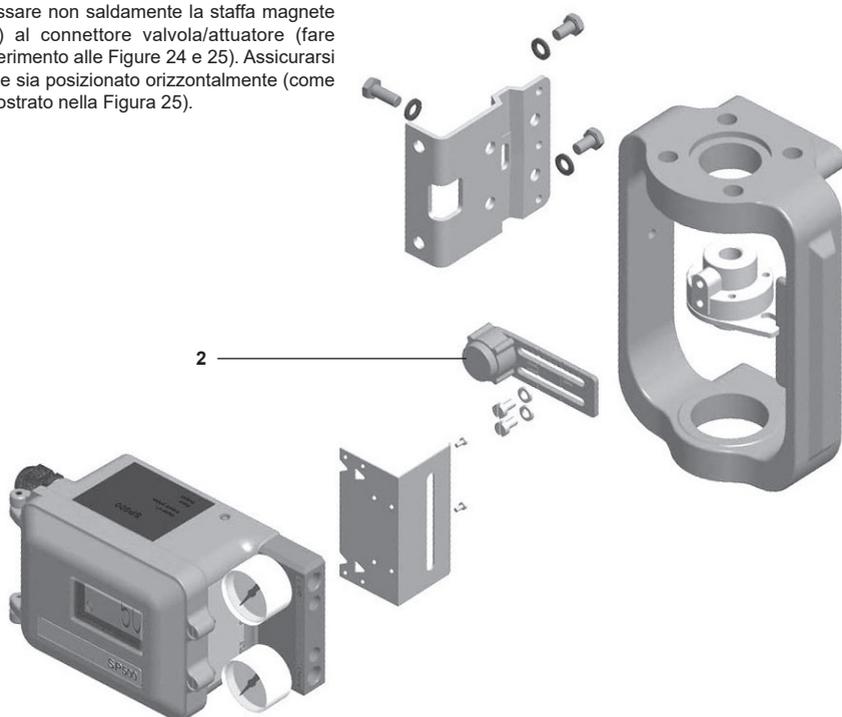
Kit di montaggio a castello per un attuatore lineare
